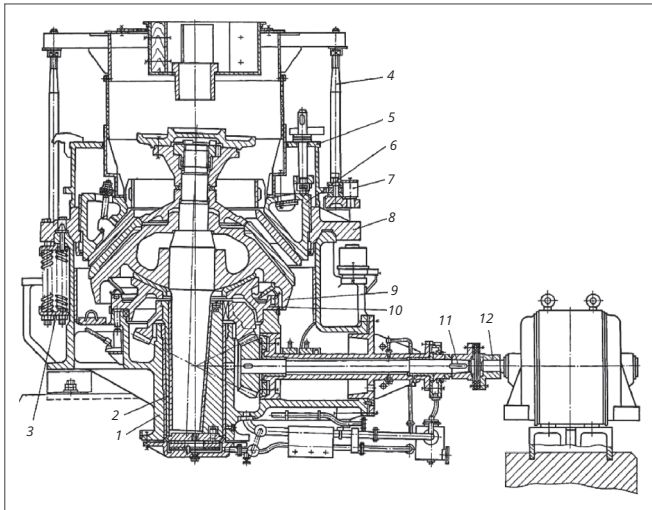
Конструкция дробилки КМД-2200: 1 – корпус; 2 – эксцентрик; 3 – пакет пружин; 4 – загрузочное устройство в сборе; 5 – кожу; 6 – регулирующее кольцо; 7 – механизм поворота; 8 – опорное кольцо; 9 – дробящий конус; 10 – опорная чаша; 11 – приводной вал; 12 – муфта
